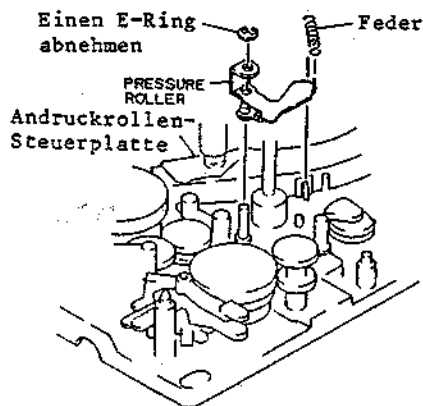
Ausbau der Andruckrollen-Steuerplatte
